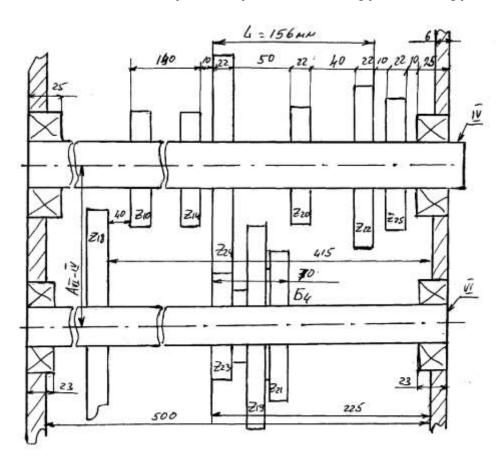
Компоновочная схема развертки наиболее нагруженной группы передач
